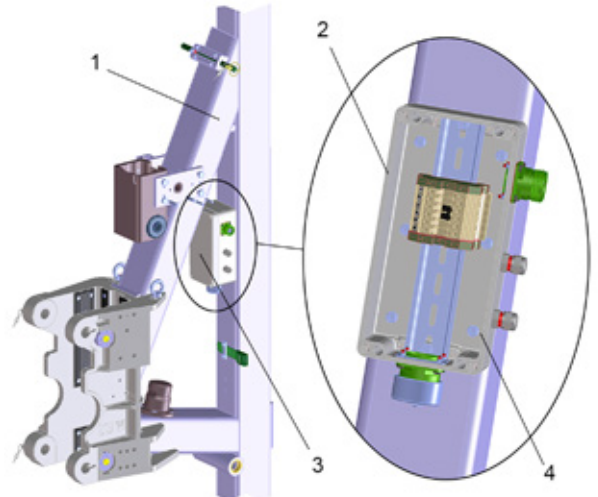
(Detailansicht ohne Deckel abgebildet)
